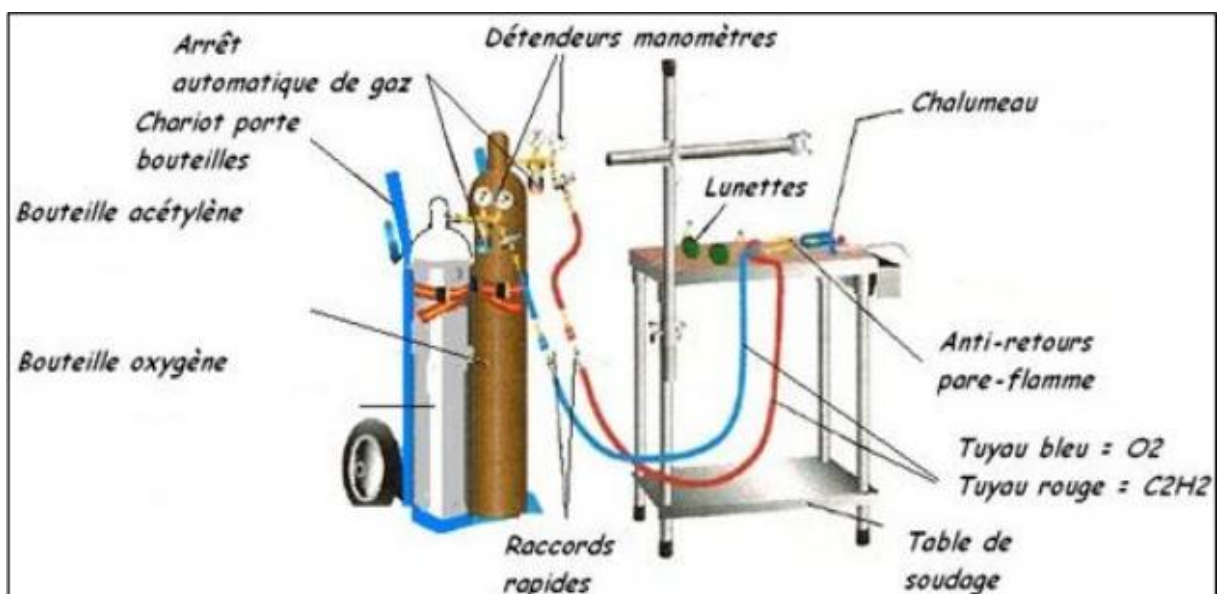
Matériel propre au soudage oxyacétylénique.
